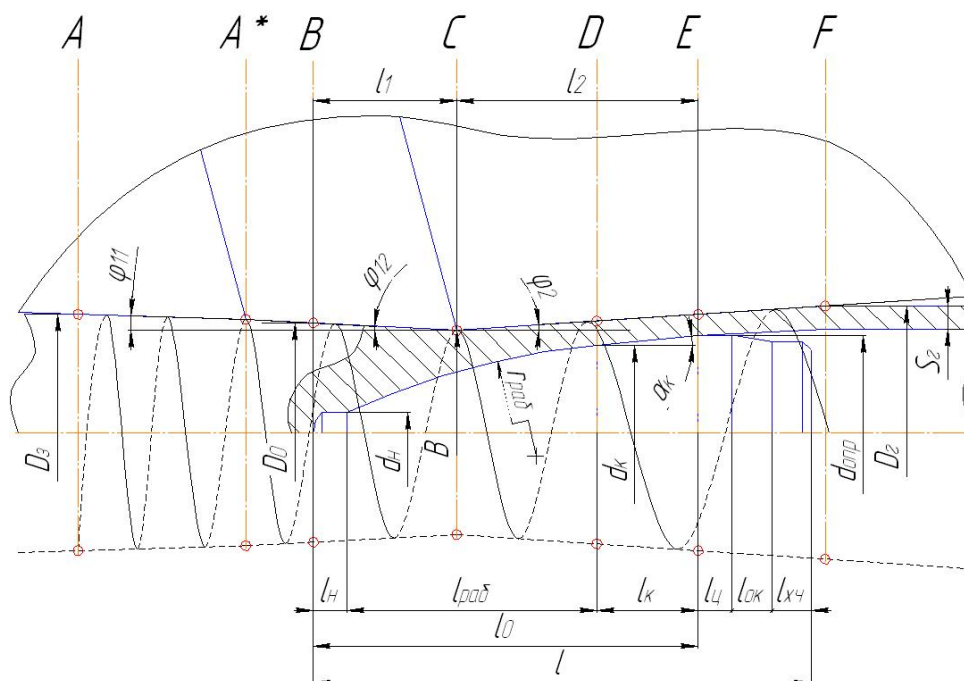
Схема для расчета калибровки оправки и настройки прошивного стана ТПА 20-168 с указанием винтового движения заготовки-гильзы [3] и характерных сечений очага деформации: A – вход заготовки в валки; A^* – начало участка повышенного обжатия; B – носок оправки; C – пережим валков; D, E – начало и конец калибрующего участка; F – выход гильзы из валков
